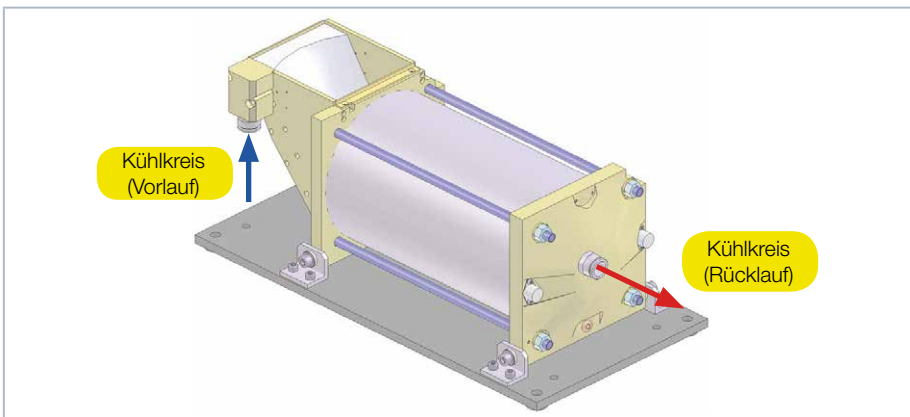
Zwei ELSA-Steckverschraubungen (Push-In)
